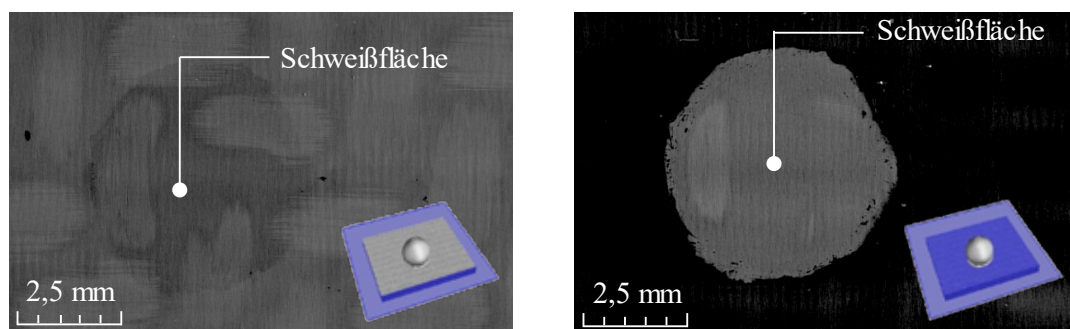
CT-Bild der Schweißverbindung PA6-CF/PA6 [138]
